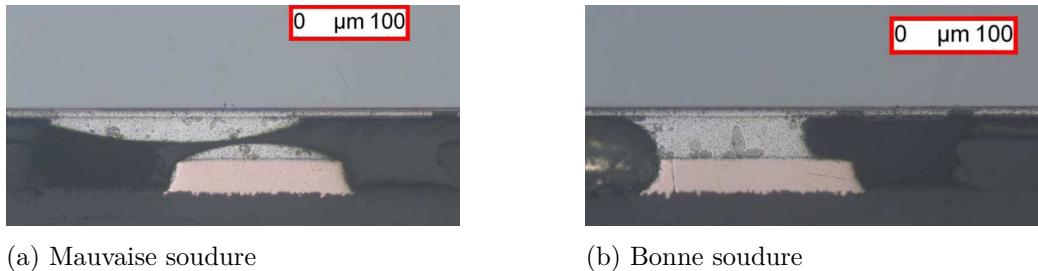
Vue en coupe des bumps du transistors GaN
